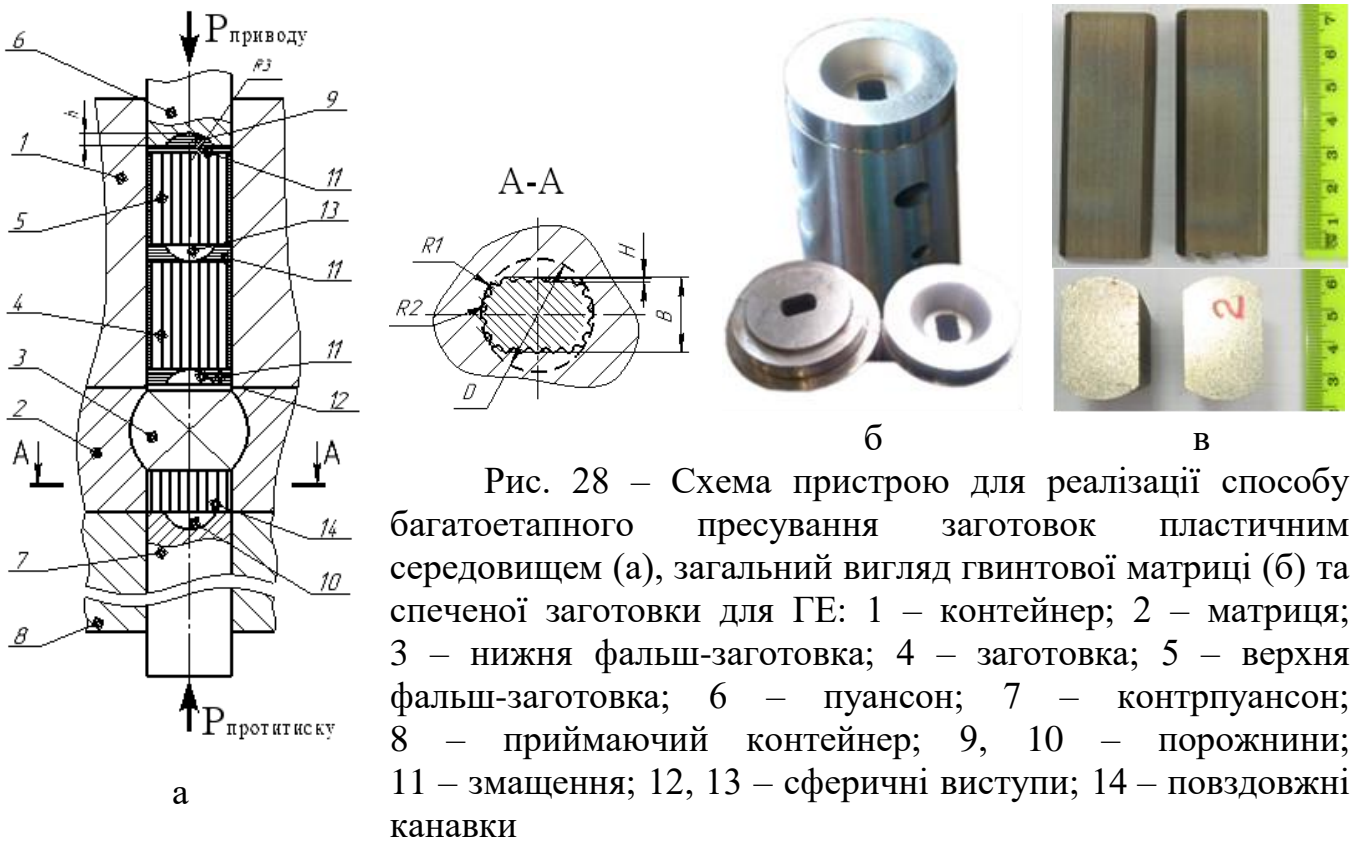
Схема пристрою для реалізації способу багатоетапного пресування заготовок пластичним середовищем (а), загальний вигляд гвинтової матриці (б) та спеченої заготовки для ГЕ: 1 – контейнер; 2 – матриця; 3 – нижня фальш-заготовка; 4 – заготовка; 5 – верхня фальш-заготовка; 6 – пуансон; 7 – контрпуансон; 8 – приймаючий контейнер; 9, 10 – порожнини; 11 – змащення; 12, 13 – сферичні виступи; 14 – повздовжні канавки
